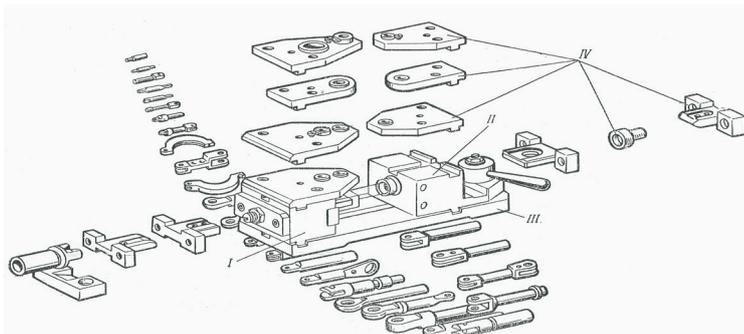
Агрегатированный базовый групповой кондуктор для сверления отверстий в деталях типа валиков и вилок: I и II – унифицированные узлы; III и IV – специальные, но не сложные по конструкции детали
